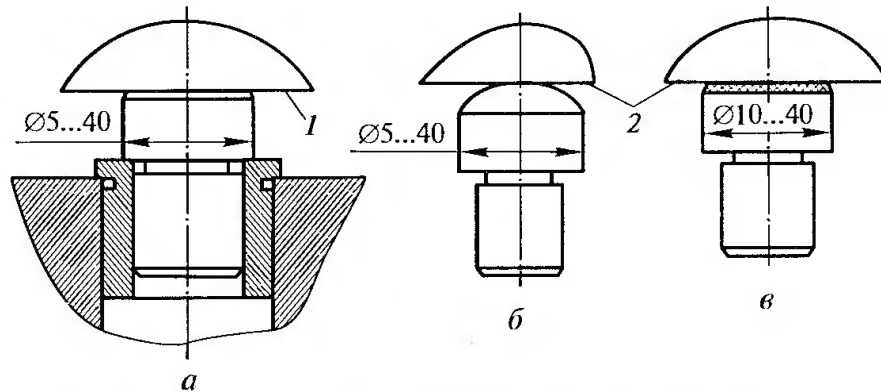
Опорні штирі з плоскою(*я*), сферичною(*б*) і насіченою (*в*) голівками: 1 — оброблена база; 2 — необроблені бази
